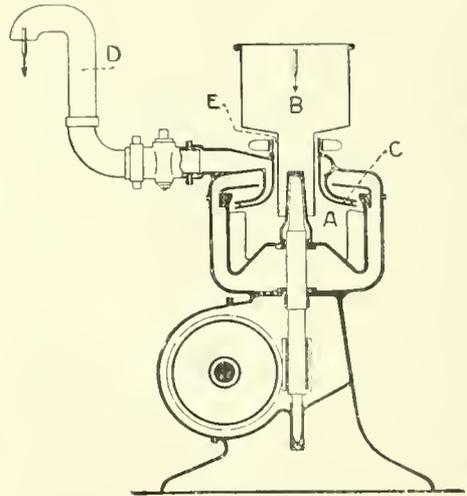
Coupe verticale du brise-mousse Astra.
